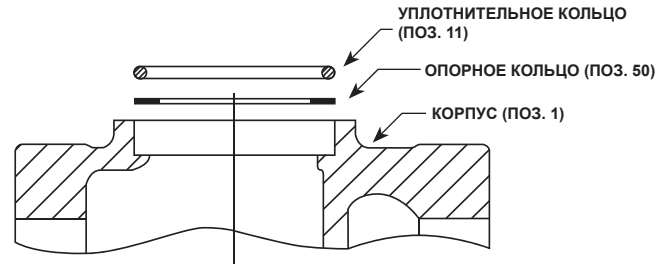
Развернутый вид корпуса, демонстрирующий расположение уплотнительного кольца и опорного кольца
